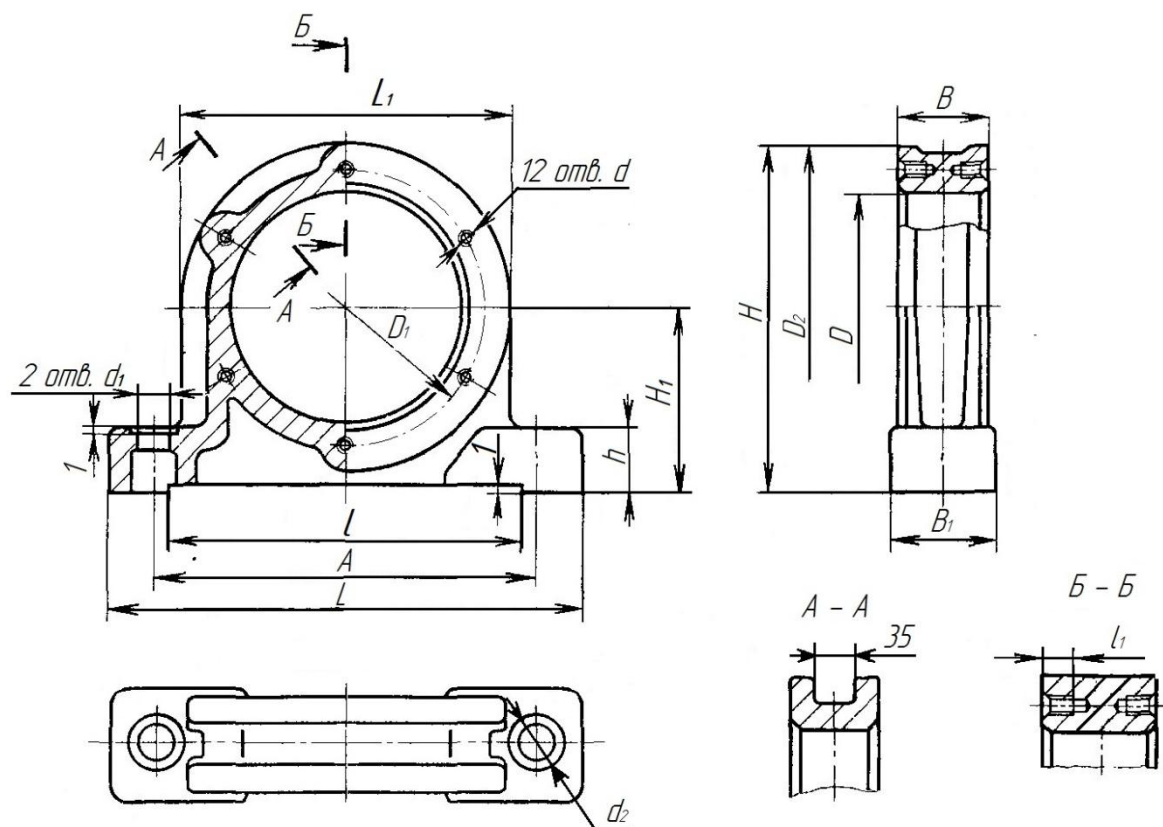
Корпуса типа УМ подшипников качения по ГОСТ 13218.4 – 80 для диаметра  $D = 160 \div 250$  мм
